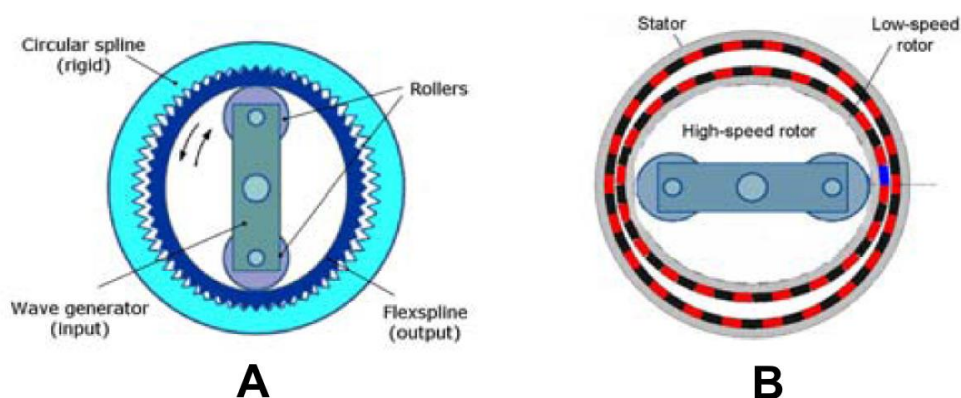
A) Engrenage harmonique mécanique. B) Engrenage harmonique magnétique [RAH7]
